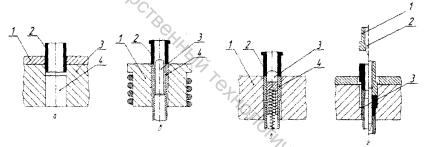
Схемы ориентировки калибруемых заготовок:
